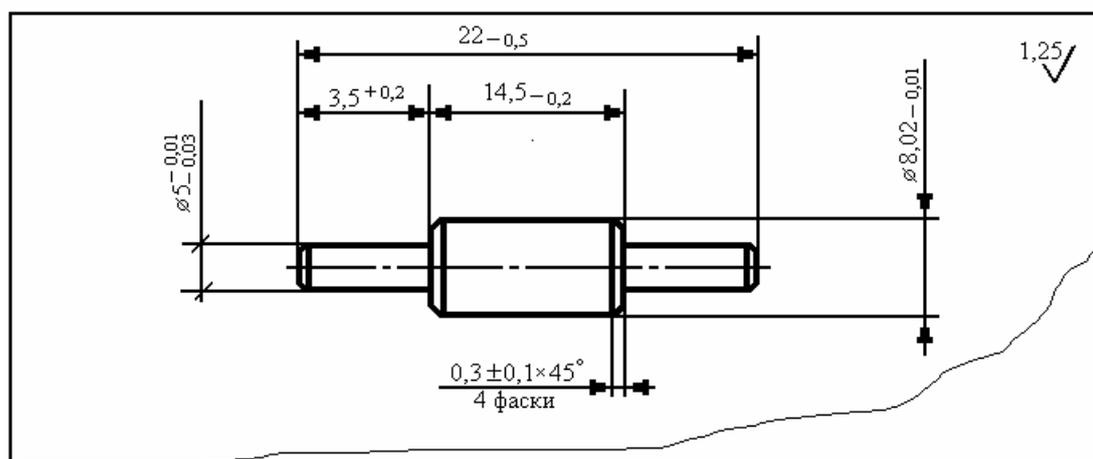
Обозначение на чертеже одного значения шероховатости поверхностей
